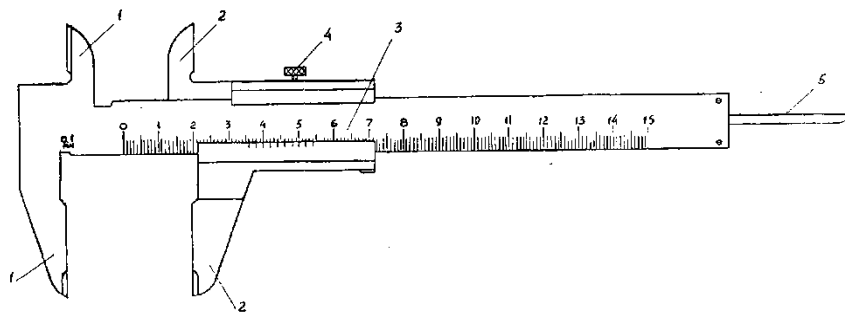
Штангенциркуль типу ШЦ-I: 1 – штанга; 2 – рамка з ноніусом (точна шкала на рамці); 3 – шкала штанги; 4 – стопорний гвинт; 5 – глибиномір
